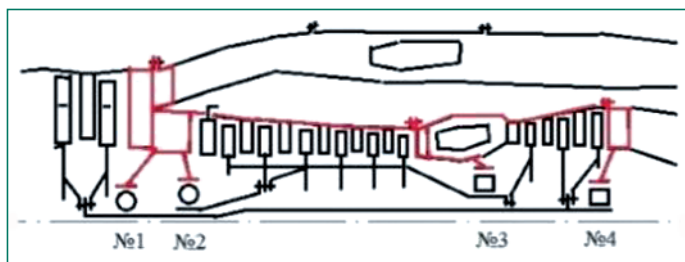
Схема расположения подшипников и опор двигателя ТРДДФ JT17A
